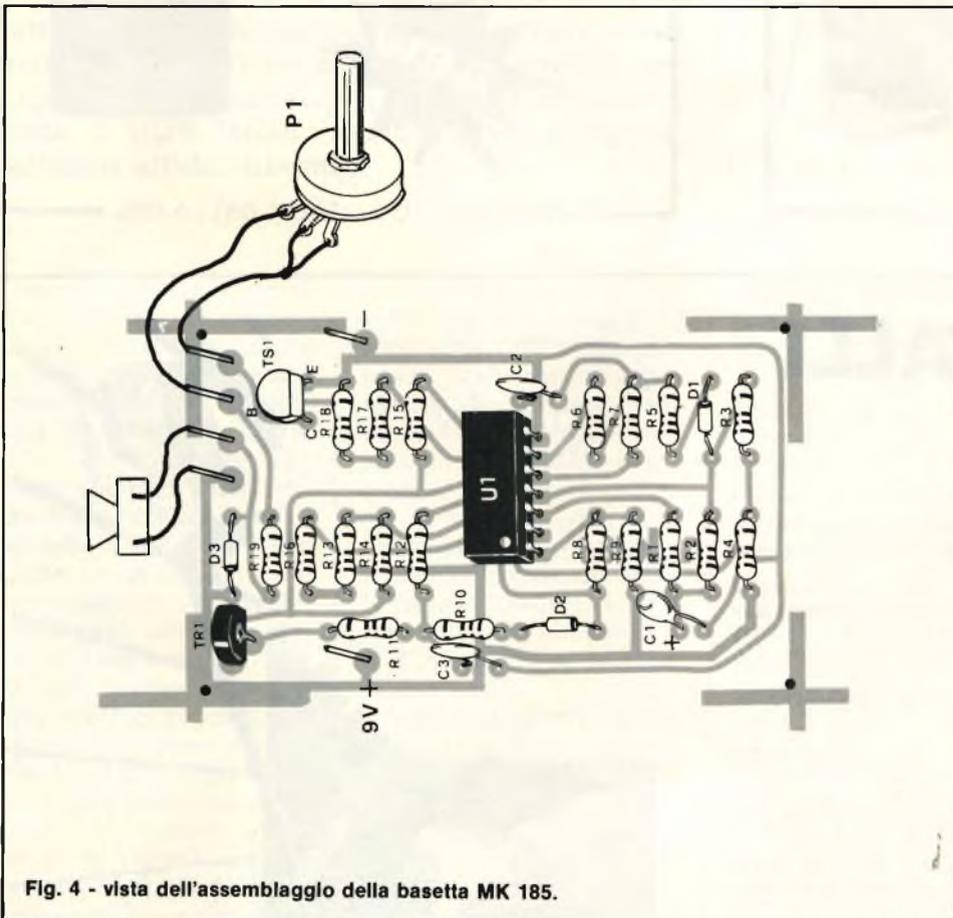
vista dell'assemblaggio della basetta MK 185.
